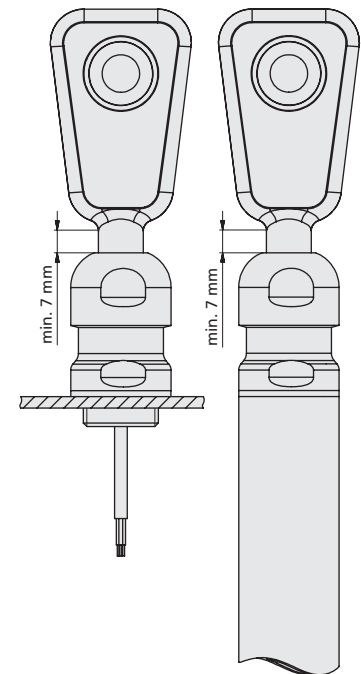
D12-Adapterschaft mit Sensorverschraubung BF-pms/A1 befestigt am Maschinenteil oder am Edelstahlrohr D26,8 mit Innengewinde M20x1,5
